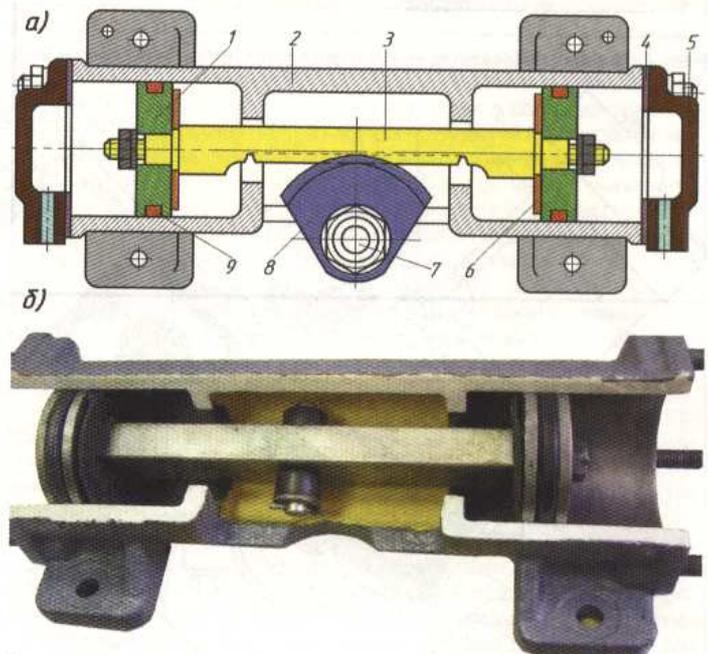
Пневматический привод реверсора 18MP электровоза ЧС2:
